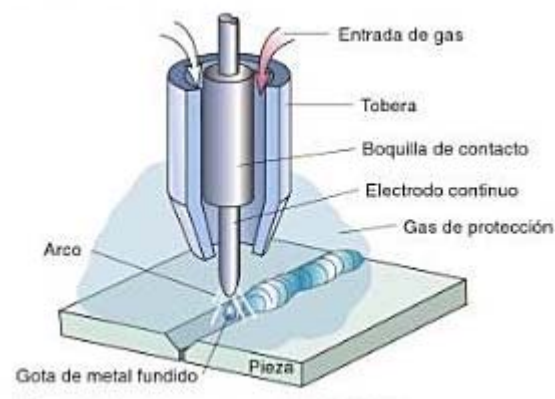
Esquema de Soldadura de MIG (*Metal Inert Gas*) y MAG (*Metal Active Gas*).
